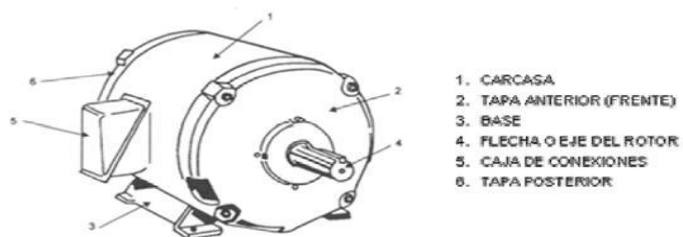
Esquema de motor monofásico con bobinado auxiliar
